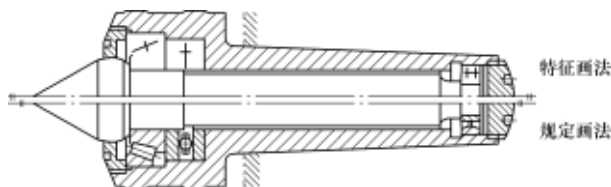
圆锥滚子轴承、推力球轴承和双列深沟球轴承在装配图中的画法
